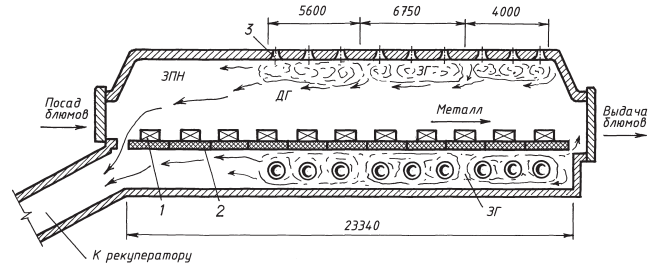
Схема нагревательной печи стана 850 РУП «БМЗ»: 1 – заготовка; 2 – шагающие балки; 3ПН – зона предварительного нагрева; ДГ – дымовые газы
